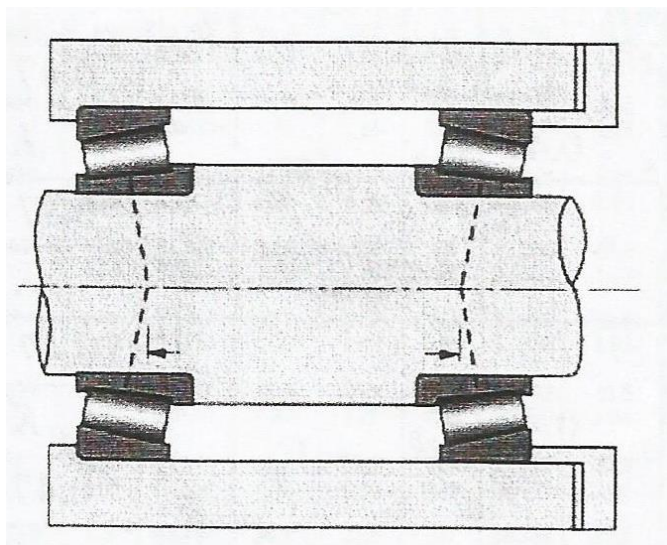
Montaje directo de rodamientos de rodillos cónicos
